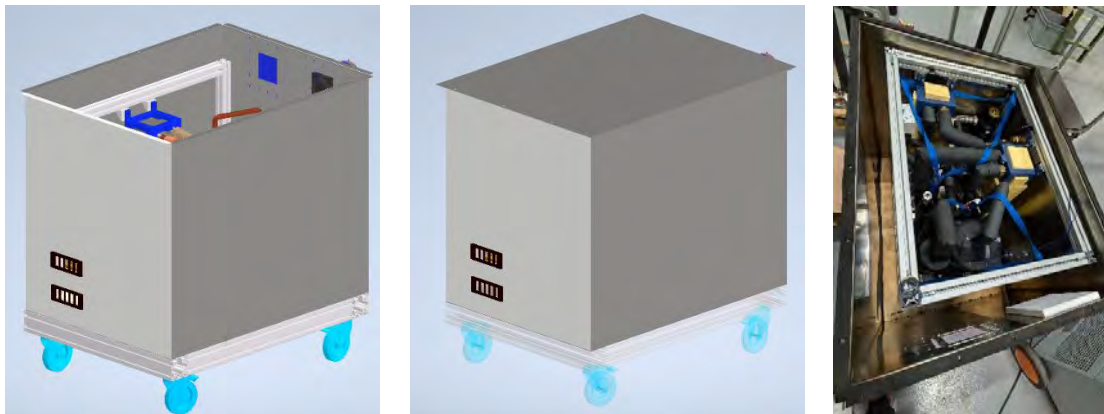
CAD-Ansicht des Schweißbehälters mit (links) und ohne (Mitte) Deckel, Dichtfläche des Deckels (rechts)
